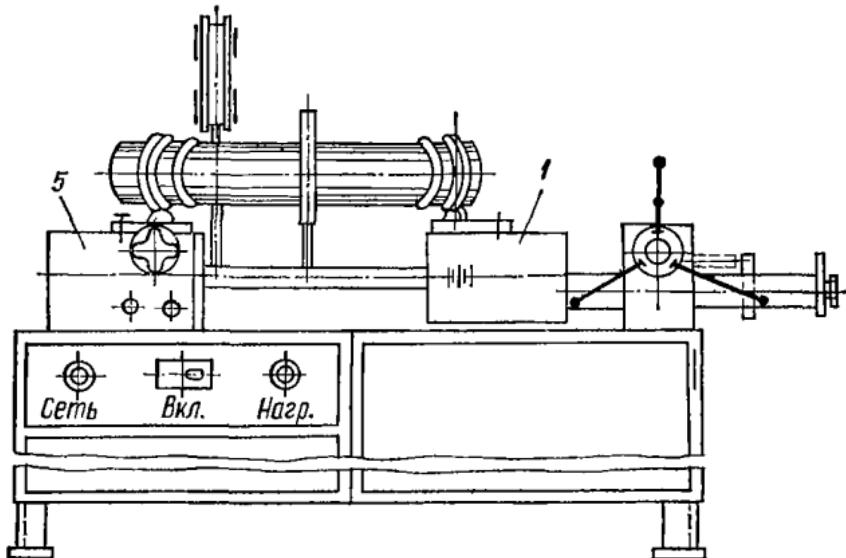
Установка УСДП-225 для сварки соединительных деталей и узлов пластмассовых трубопроводов:
